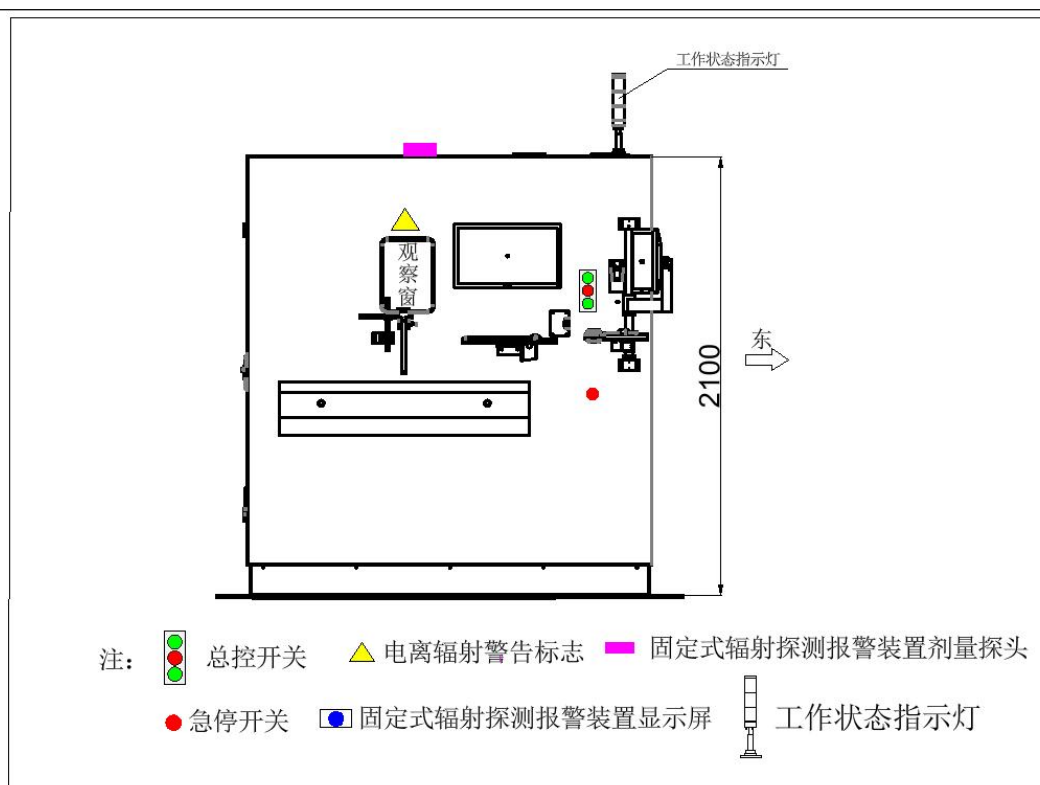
(a) 本项目 4#工业 CT 机 (L2161 型) 平面布置图
